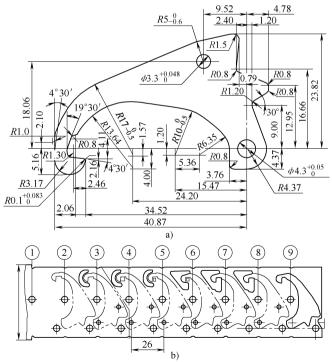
拨叉级进模 a) 零件图 b) 排样图
